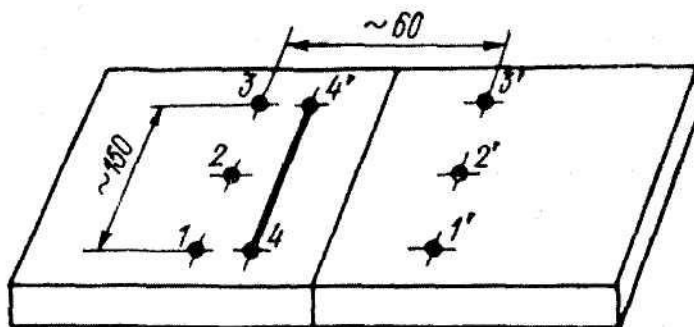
Разметка пробы перед сваркой для определения укорочения
